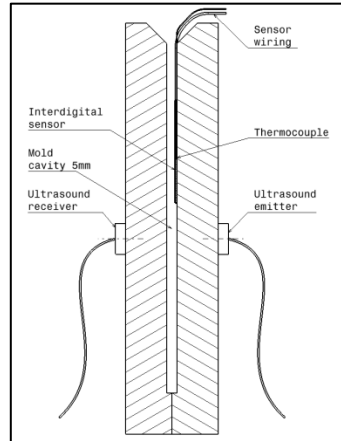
Schnittansicht des Testwerkzeuges mit Sensorpositionen
